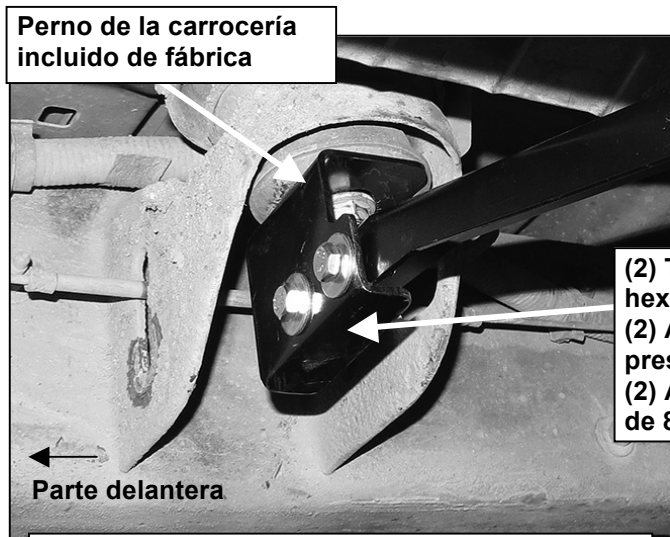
A) Ensamblaje del soporte central izquierdo/del lado del conductor
